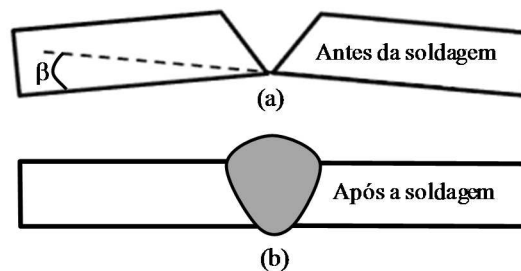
(a) Pré-desalinhamento antes da soldagem com o valor do ângulo da distorção β que será produzido na soldagem e (b) Peças alinhadas e sem distorção angular após a soldagem.
